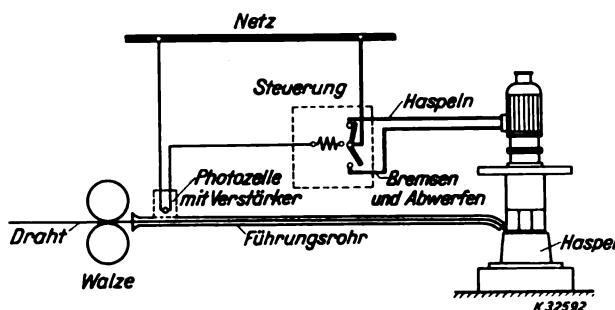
Eine lichtelektrische Drahthaspelsteuerung.
